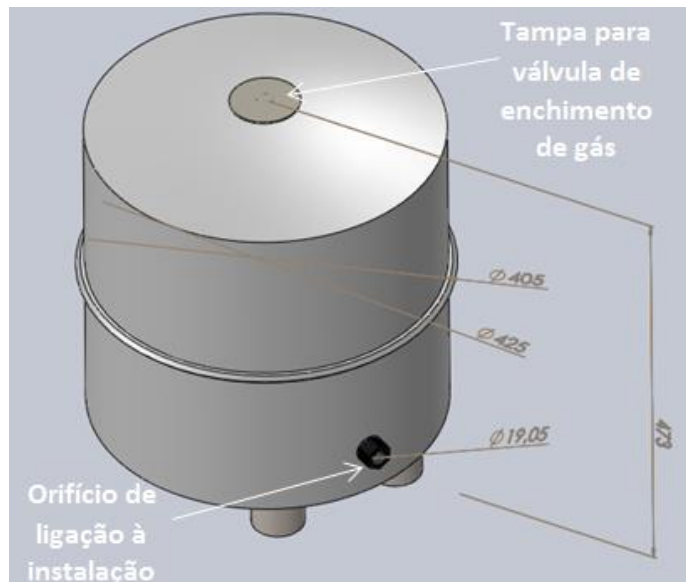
Desenho tridimensional do vaso de expansão e respetivas dimensões geométricas.
